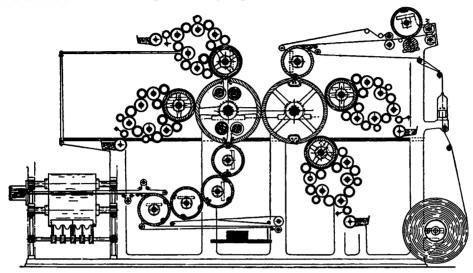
Billettdruck-Rotationsmaschine der Fabrik Frankenthal
